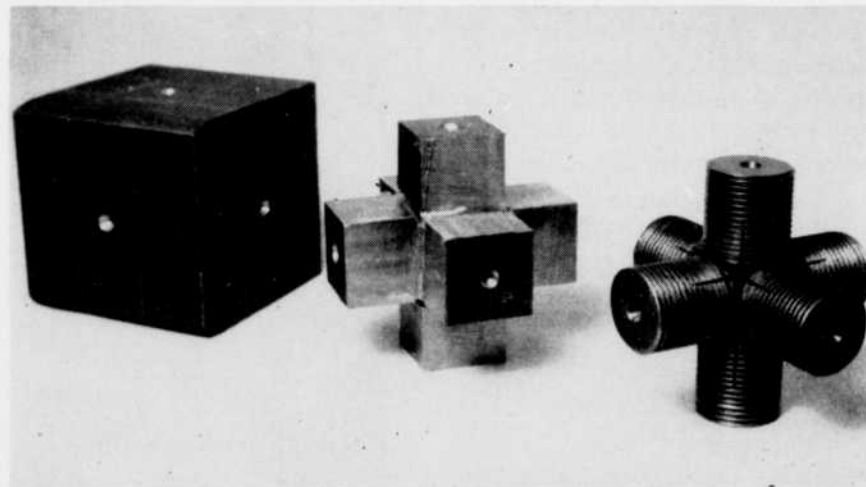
L'éprouvette triaxiale et ses étapes d'usinage.
